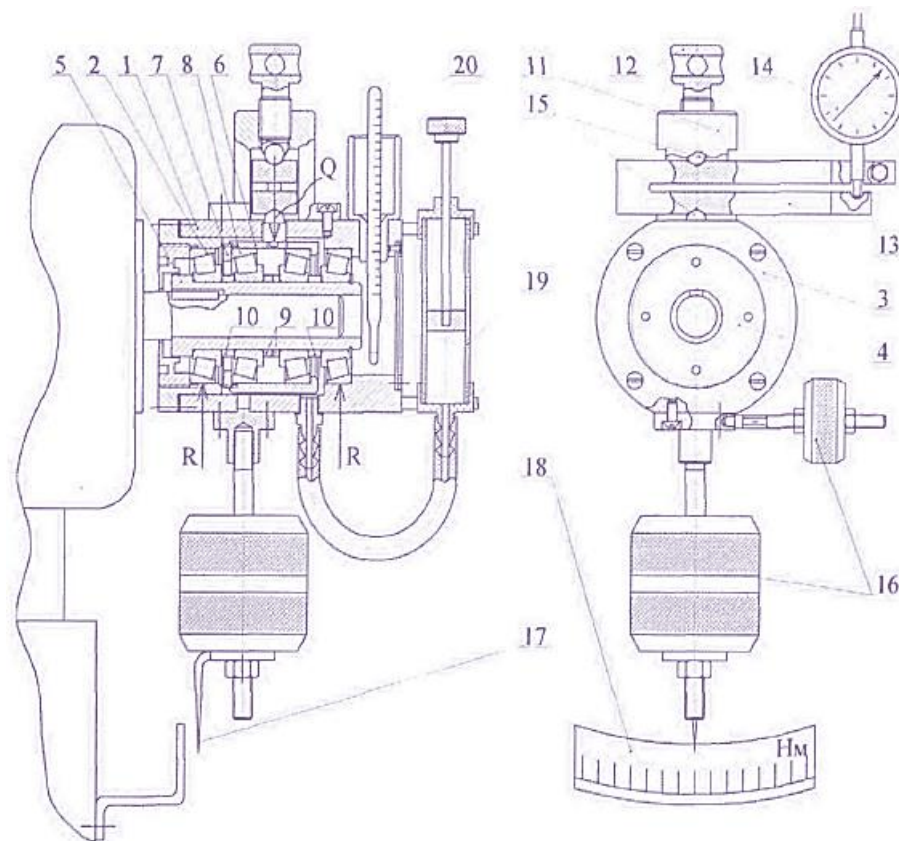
Схема лабораторної установки ДМ-28 з підшипниковим вузлом, що випробовується: 1 - корпус підшипникового вузла, що випробовується; 2 - конічний роликпідшипник; 3 – кришка підшипникового вузла; 4 - гайка торцева; 5 – монтажна втулка; 6 - корпус вузла, що навантажується; 7 – регульовальна гайка; 8 - роликпідшипник навантажуваного вузла; 9, 10 – розпірна втулка; 11 - скоба наполеглива; 12 - гвинт навантажувальний; 13 - динамічна скоба; 14 – індикатор годинного типу; 15 - кулька центрувальна; 16 - маятник; 17 - стрілка маятника; 18 – шкала; 19 - масляний циліндр; 20 – термометр.
